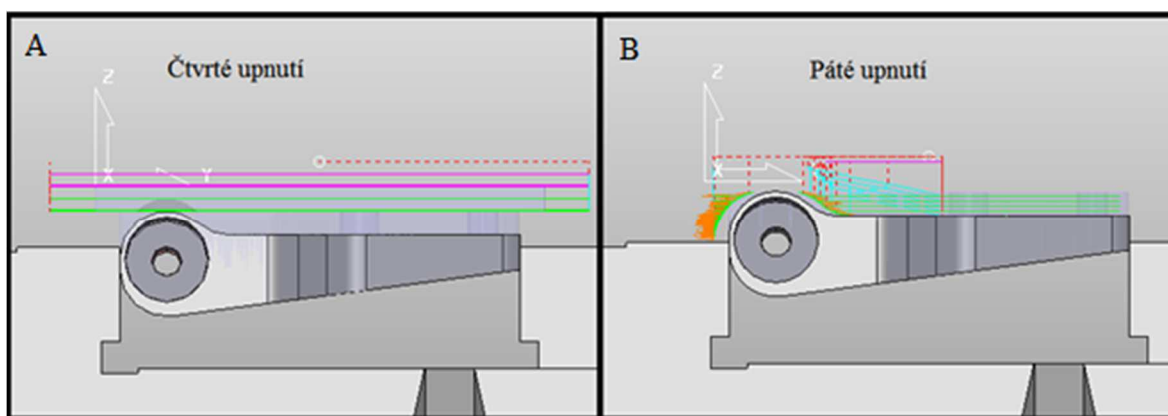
Ustavování polotovaru a odměřování nulového bodu.
